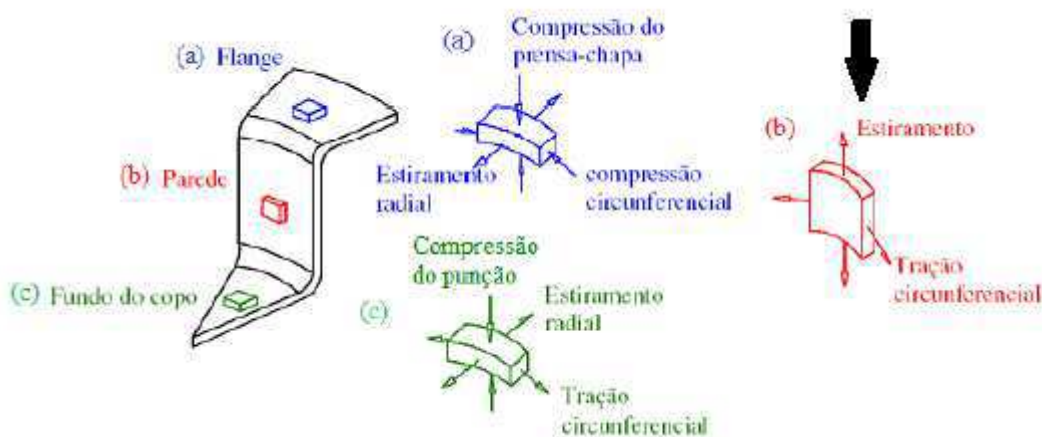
Sentido de aplicação de força para estado de tensão plano.
